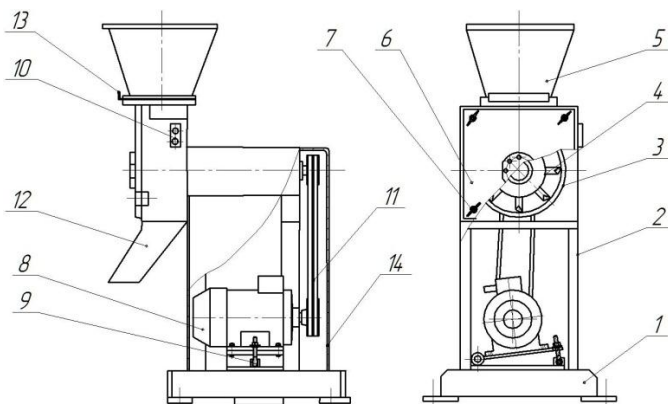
Загальний вигляд зернової молоткової дробарки: 1 – основа; 2 – корпус; 3 – сито; 4 – ротор; 5 – бункер; 6 – щит; 7 – гвинт; 8 – електродвигун; 9 – натяжний пристрій; 10 – пульт керування; 11 – паси; 12 – вивантажувальний патрубок; 13 – шиберна заслінка; 14 – захисний кожух
